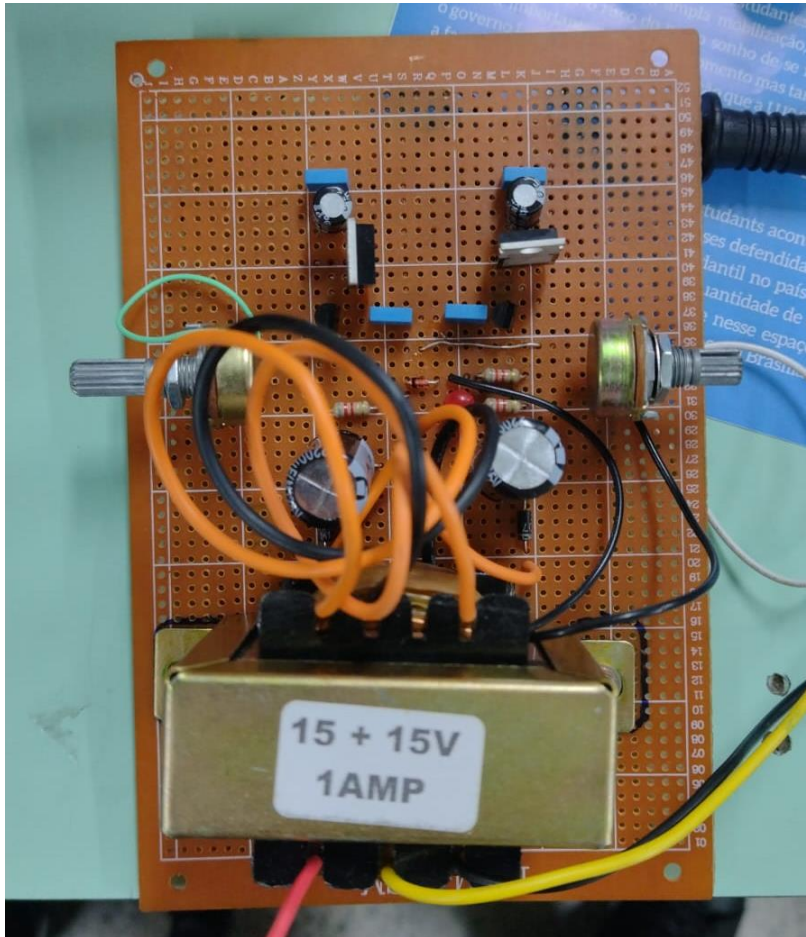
Foto de montagem de fonte de alimentação simétrica
